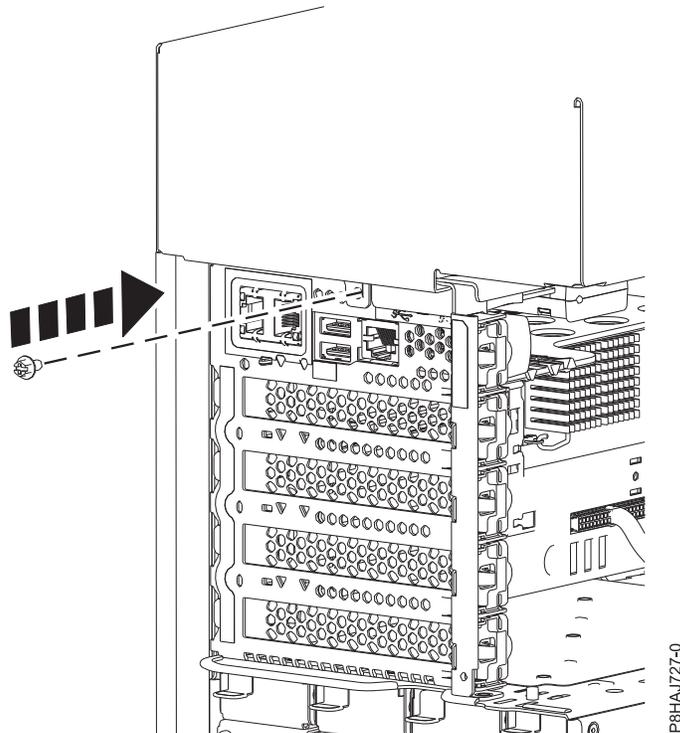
Anbringen der Schraube der Seitenabdeckung bei einem Standalone-System vom Typ 8286-41A
